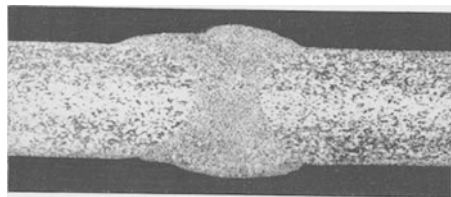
Aluminiumblechschweißung, mit Reinaluminiumdraht geschweißt und warm gehämmert.
